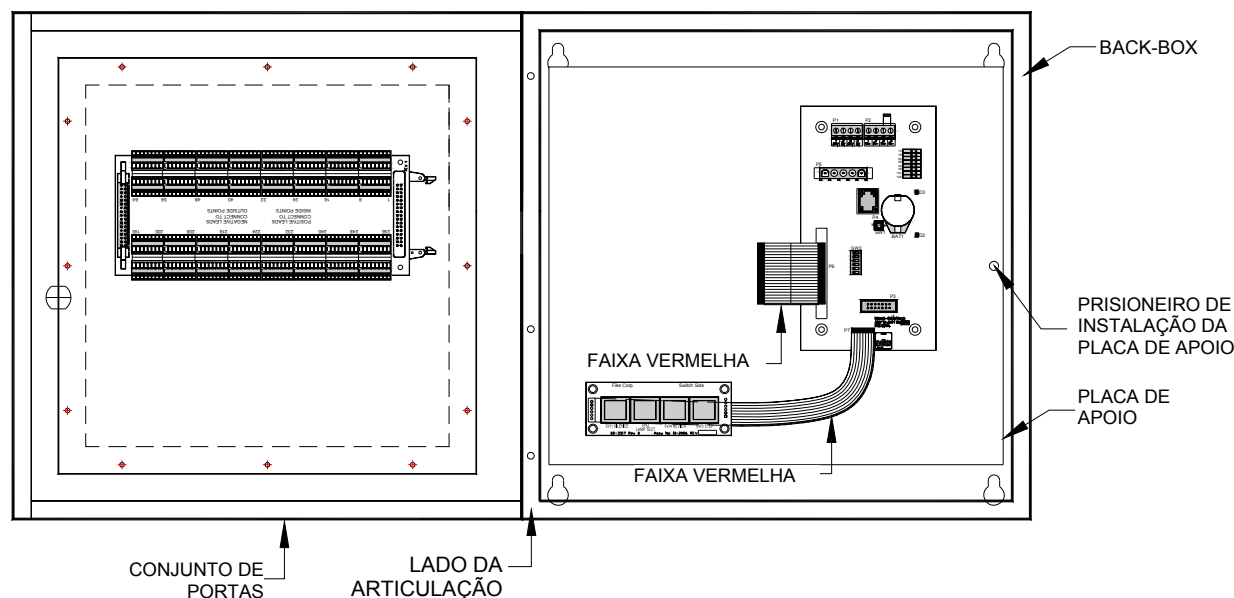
Conjunto de portas e instalação da placa de apoio
